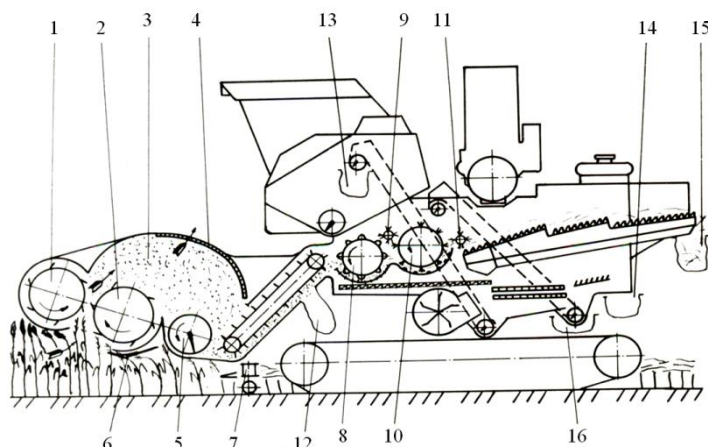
Конструктивно-технологическая схема экспериментального комбайна с двухбарабанным МСУ: 1, 2 – очесывающие барабаны; 3 – камера; 4 – сетка; 5 – шнек; 6 – нижний кожух; 7 – режущее устройство; 8 – штифтовый ротационный барабан; 9 – промежуточный битер; 10 – молотильный барабан; 11 – отбойный битер; 12, 13, 14 – пробоотборники
